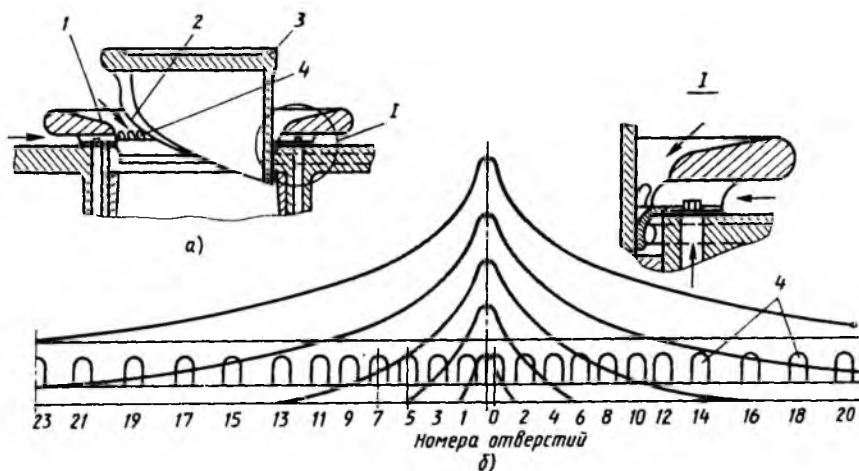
Схема распыливающей части карбюратора с переменным сечением воздушного канала и изменяемым количеством отверстий распылителя и раз-
